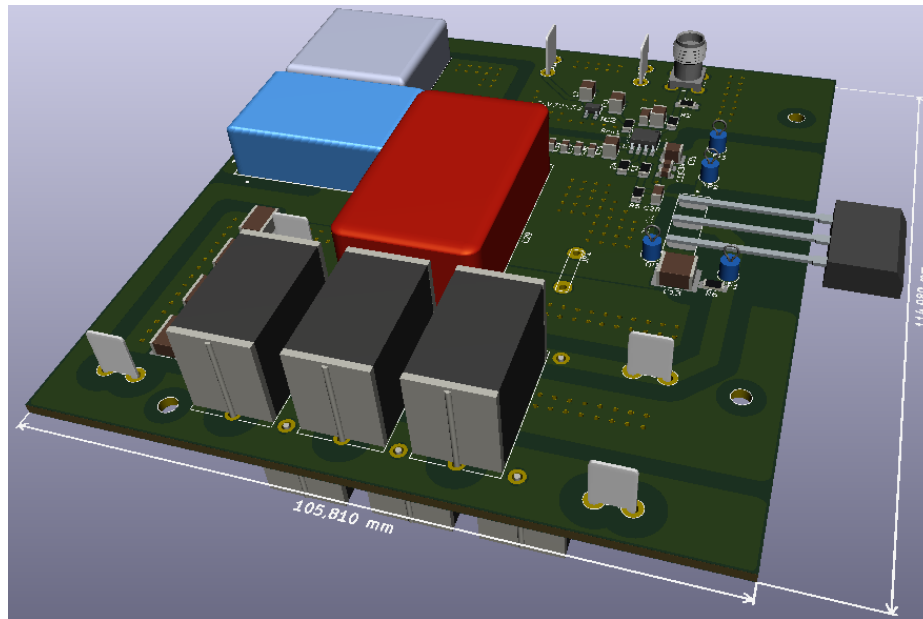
Vista en perspectiva de la parte superior del diseño de PCB en 3D
